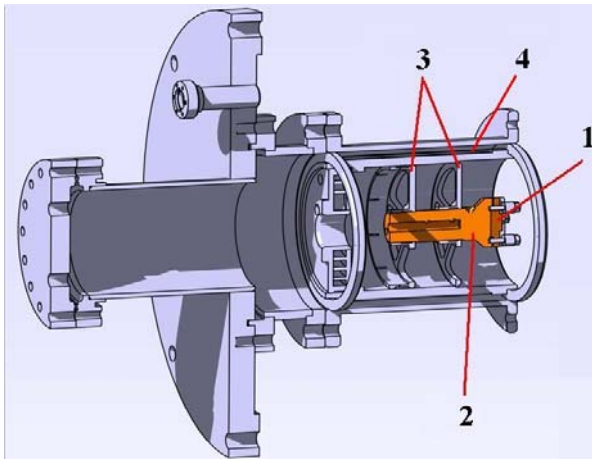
Мишенный блок: 1 – сборка-держатель образцов; 2 – медная болванка; 3 – спицы из нержавеющей стали; 4 – система водяного охлаждения
